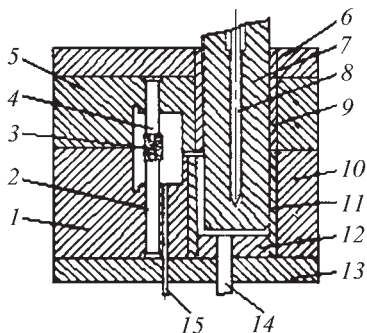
Конструкция штампа для производства детали «поворотный шарнир» из алюминиевого сплава методом реоштамповки:
